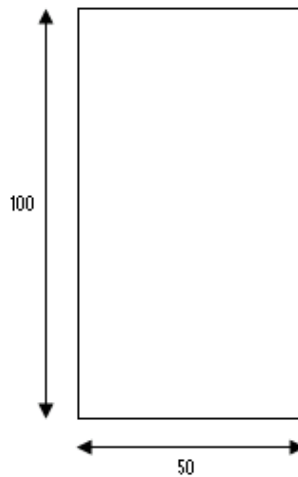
Dimensiones del cupón de soldadura en mm.
